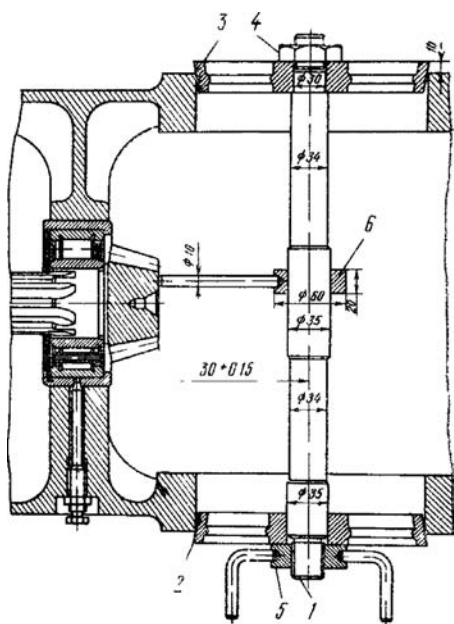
Приспособление для рег. улировки положения шестерни вторичного вала коробки передач: 1 — вал; 2 — центрирующий конус подвижный; 3 — центрирующий конус неподвижный; 4 — гайка; 5 — зажимная гайка; 6 — кольцо с контрольным штифтом
